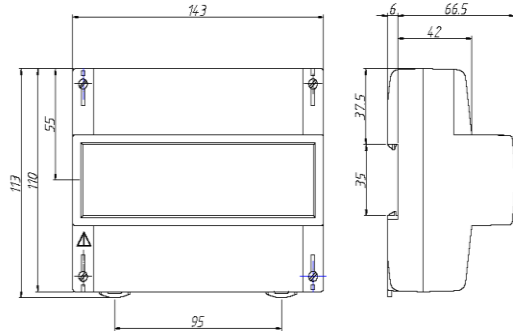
Загальний вигляд лічильника ЦЭ6804-U у корпусі Р31
